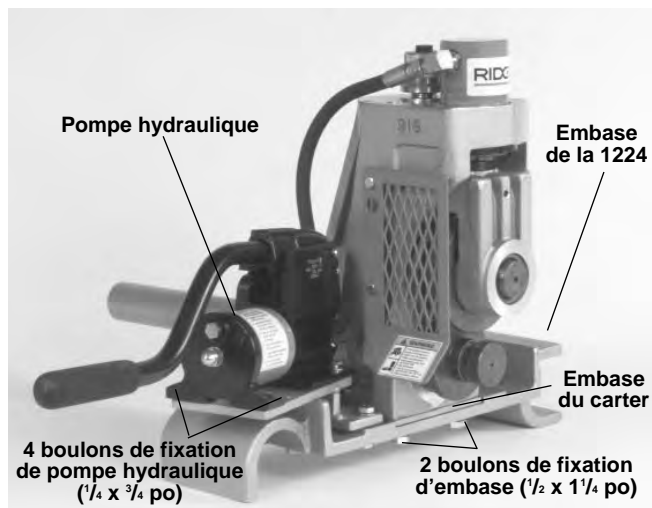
Rainureuse à galets industrielle n° 918 sur embase de machine à fileter n° 1224
